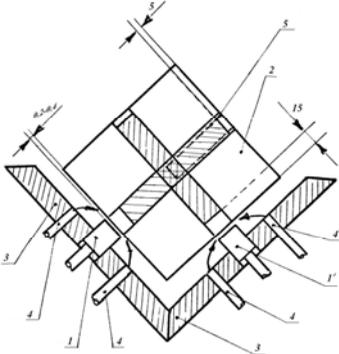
Тестовая заготовка для ультразвуковой установки (обозначения в тексте)
